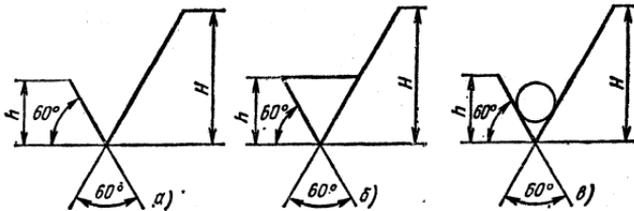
Типы знаков для обозначения шероховатости поверхности:
